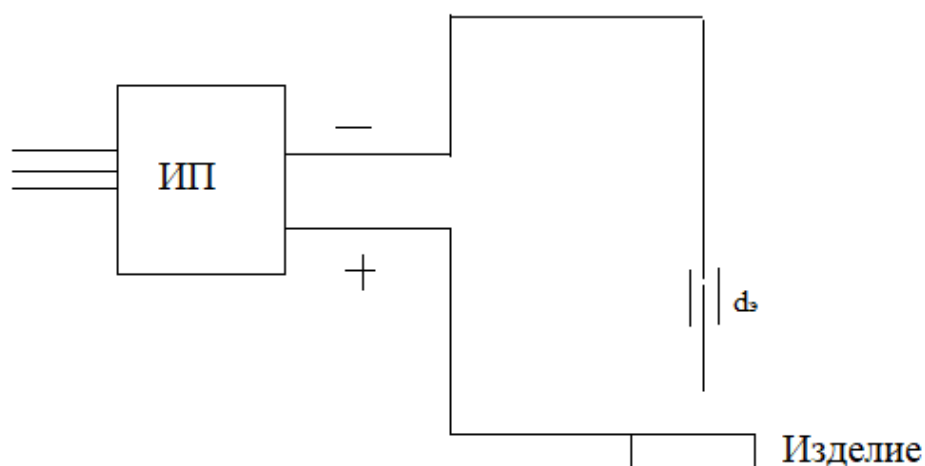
Упрощенная схема сварочного поста
